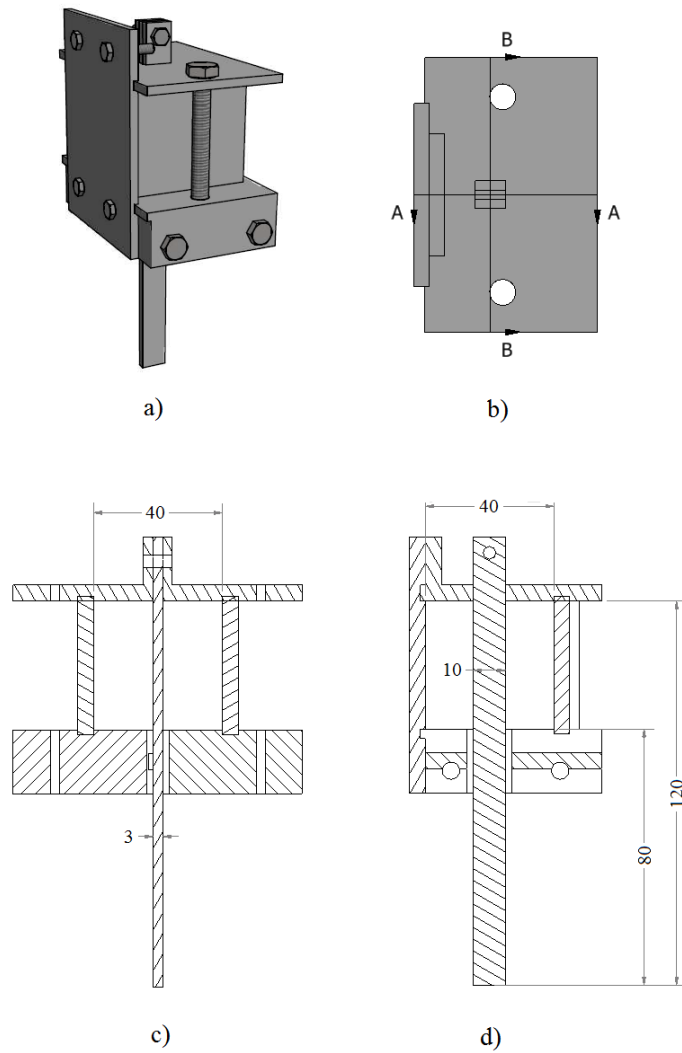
a) imagem tridimensional do molde; b) Planta com identificação dos cortes A e B; c) Corte B (dimensões em mm) e d) Corte A (dimensões em mm).
